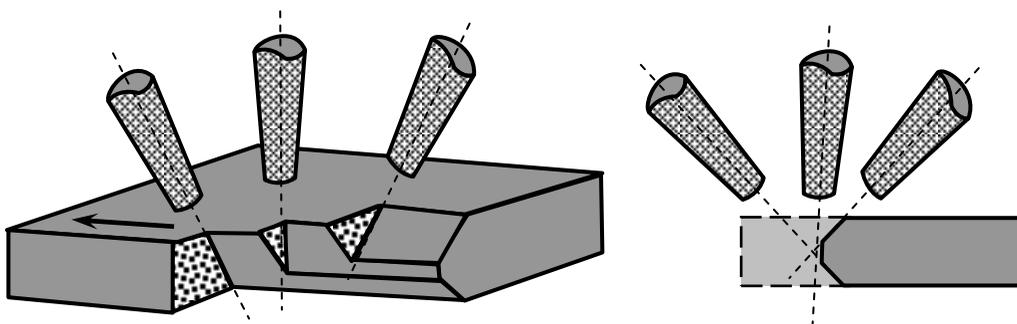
Схема разделительной резки с одновременной подготовкой кромок под сварку
